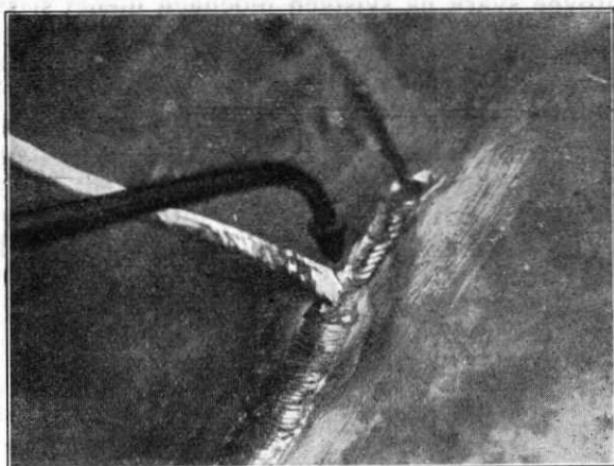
Sváření 10 mm silného olověného plechu směrem vzhůru.
